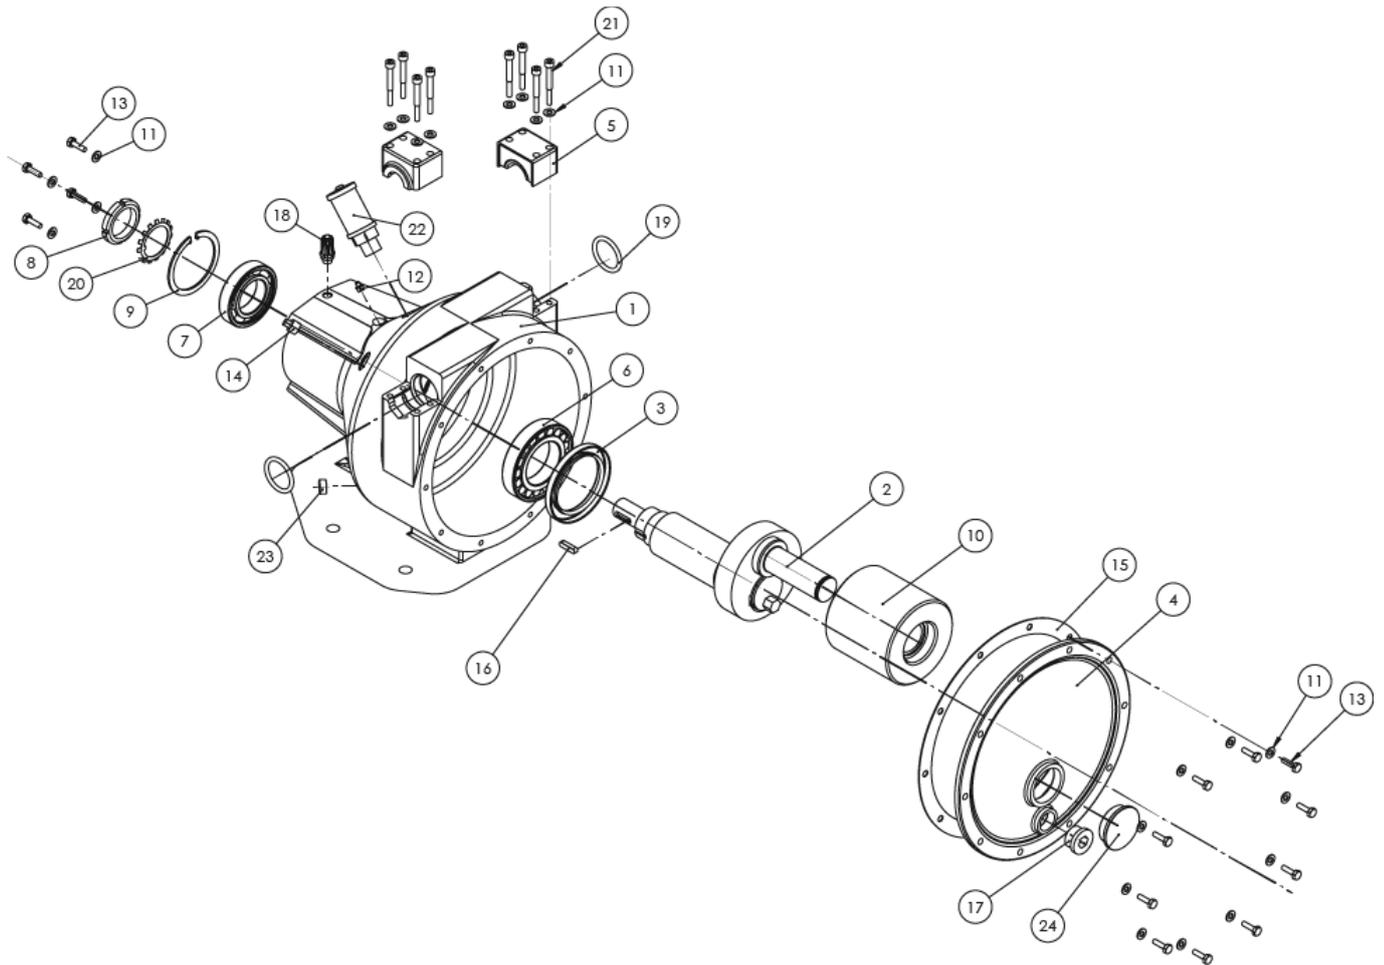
Explosionszeichnung der gesamten LPP-D-Pumpe
